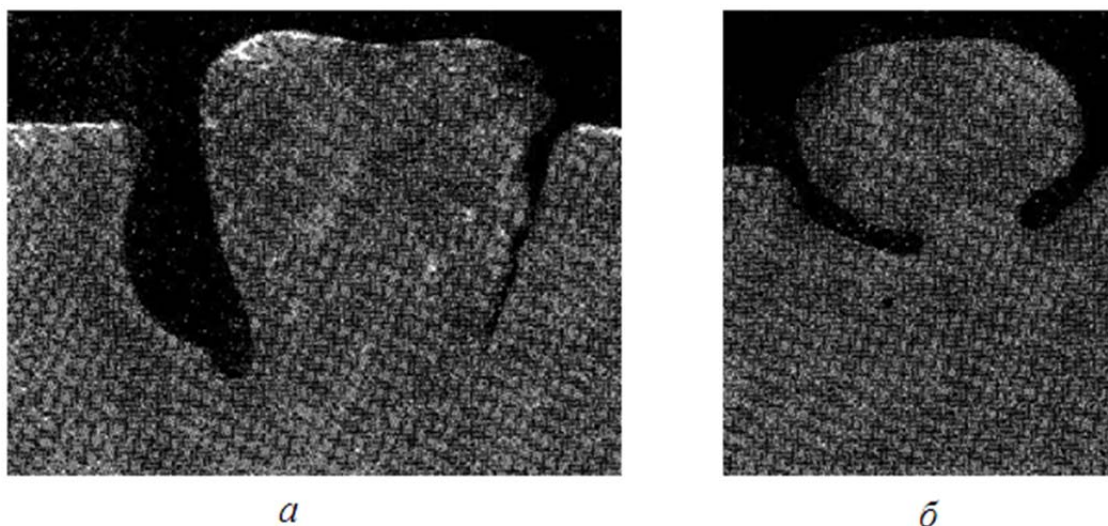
Зона несплавлення при дуговому зварюванні
